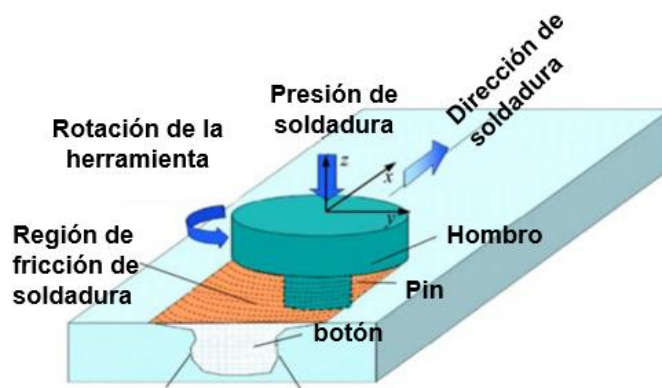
1 Pin. Herramienta para realizar la soldadura por FSW.
